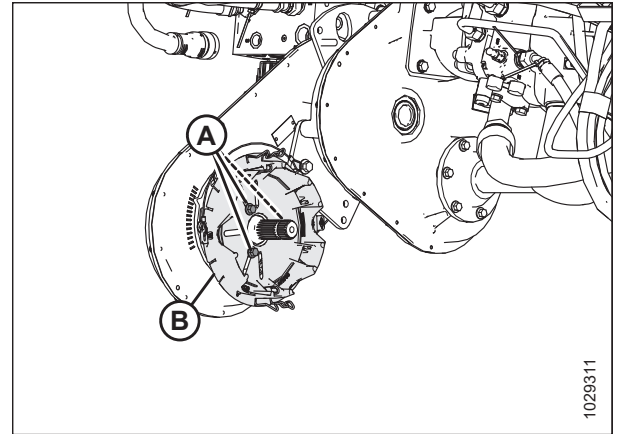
Кришка натягувача ланцюга знижувального редуктора
